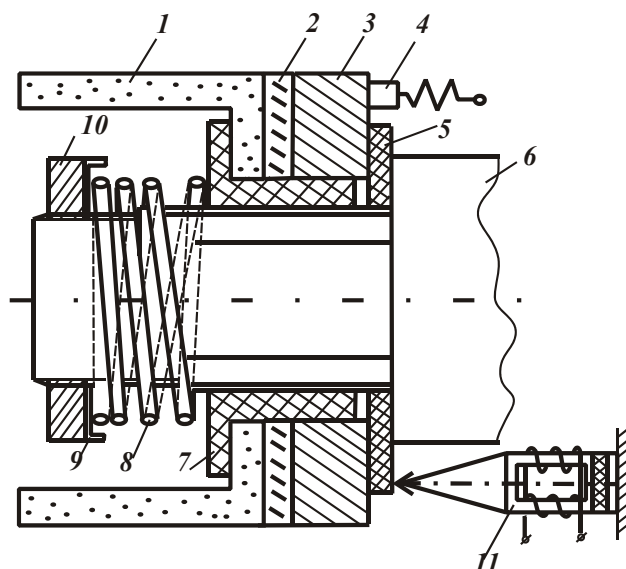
Схема ультразвукового шлифования: 1 – чашечный круг; 2 – пьезоэлектрический диск; 3 – металлическая шайба; 4 – токоподводящая и токосъемная щетки; 5 – текстолитовая шайба; 6 – вал со шлицами и резьбой; 7 – текстолитовая шлицевая втулка; 8 – пружина; 9 – шайба; 10 – гайка; 11 – магнестрикционная колебательная система.
